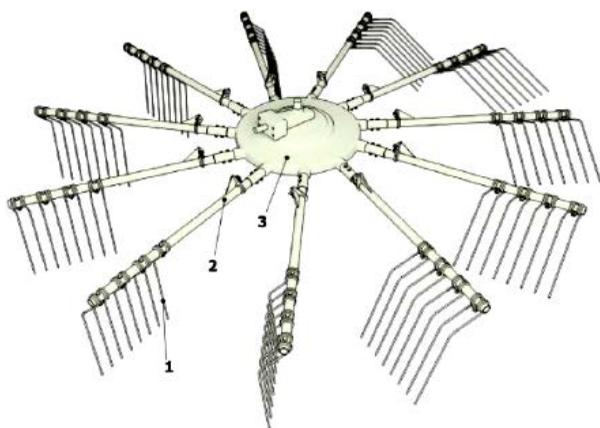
Ротор: 1 – граблина; 2 – штанга; 3 – редуктор
